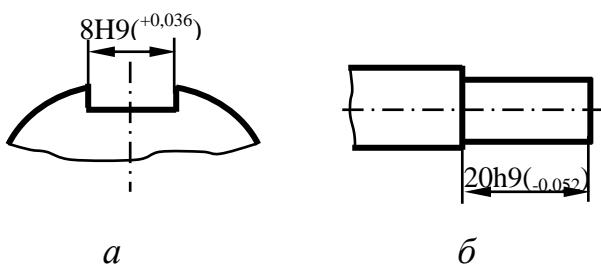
Випадки обов'язкової вказівки в кресленнях полів допусків разом із граничними відхиленнями
